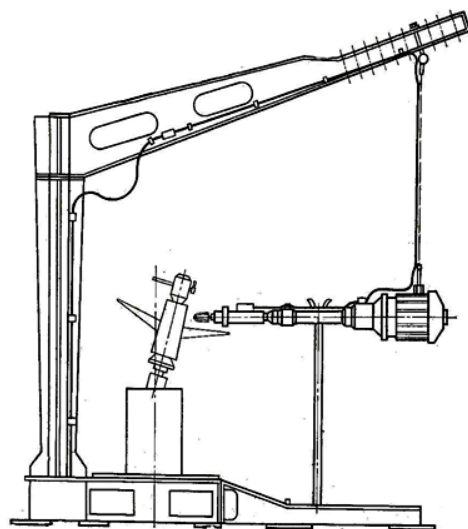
Стенд для наплавлення і обробки лопатей гребних гвинтів
